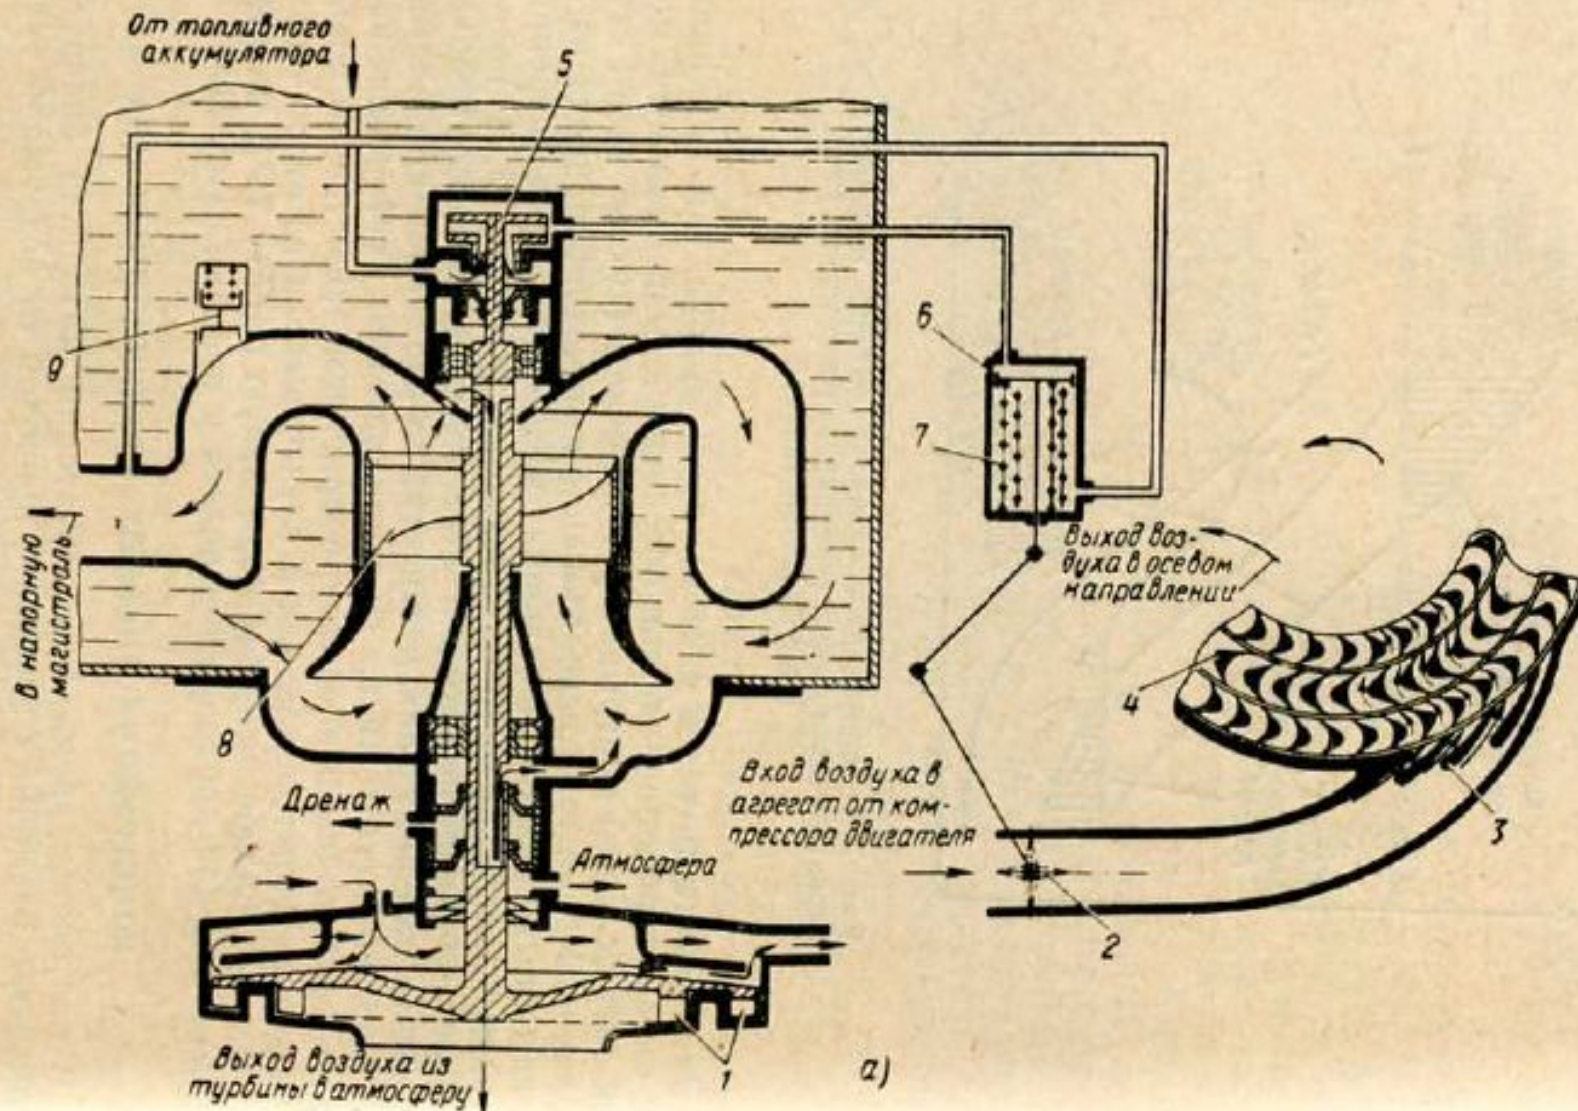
Типовая конструкция двигателя для привода внутрибакового ЭЦН:
